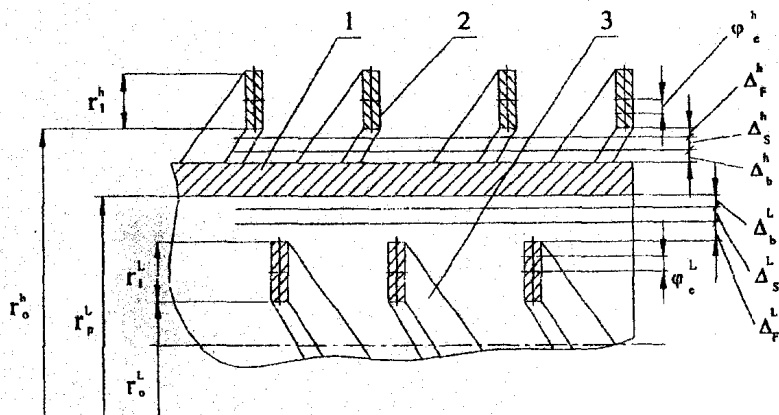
Розрахункова схема для визначення умов закріплення заготовки (втулки):
